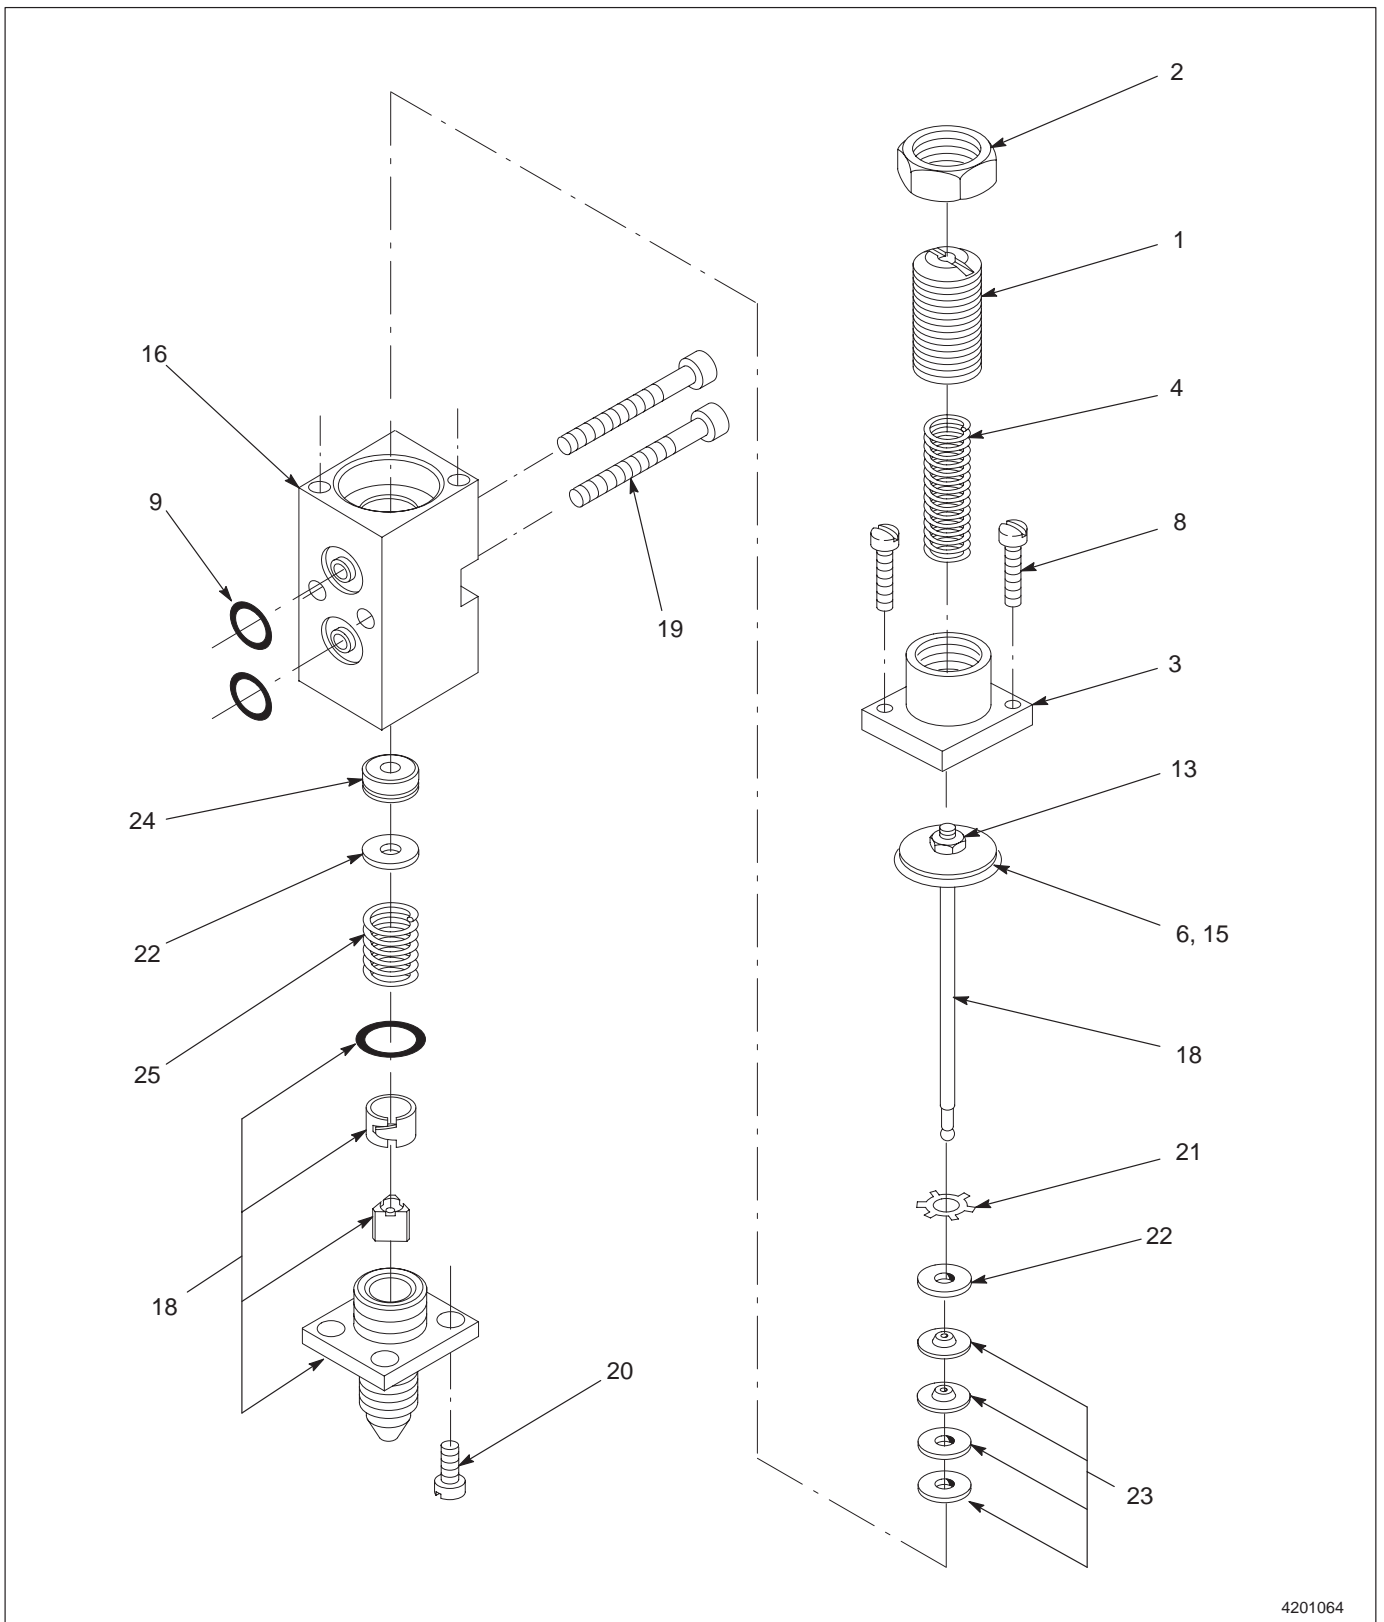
Pièces d'un module H-200 à cavité minimum
